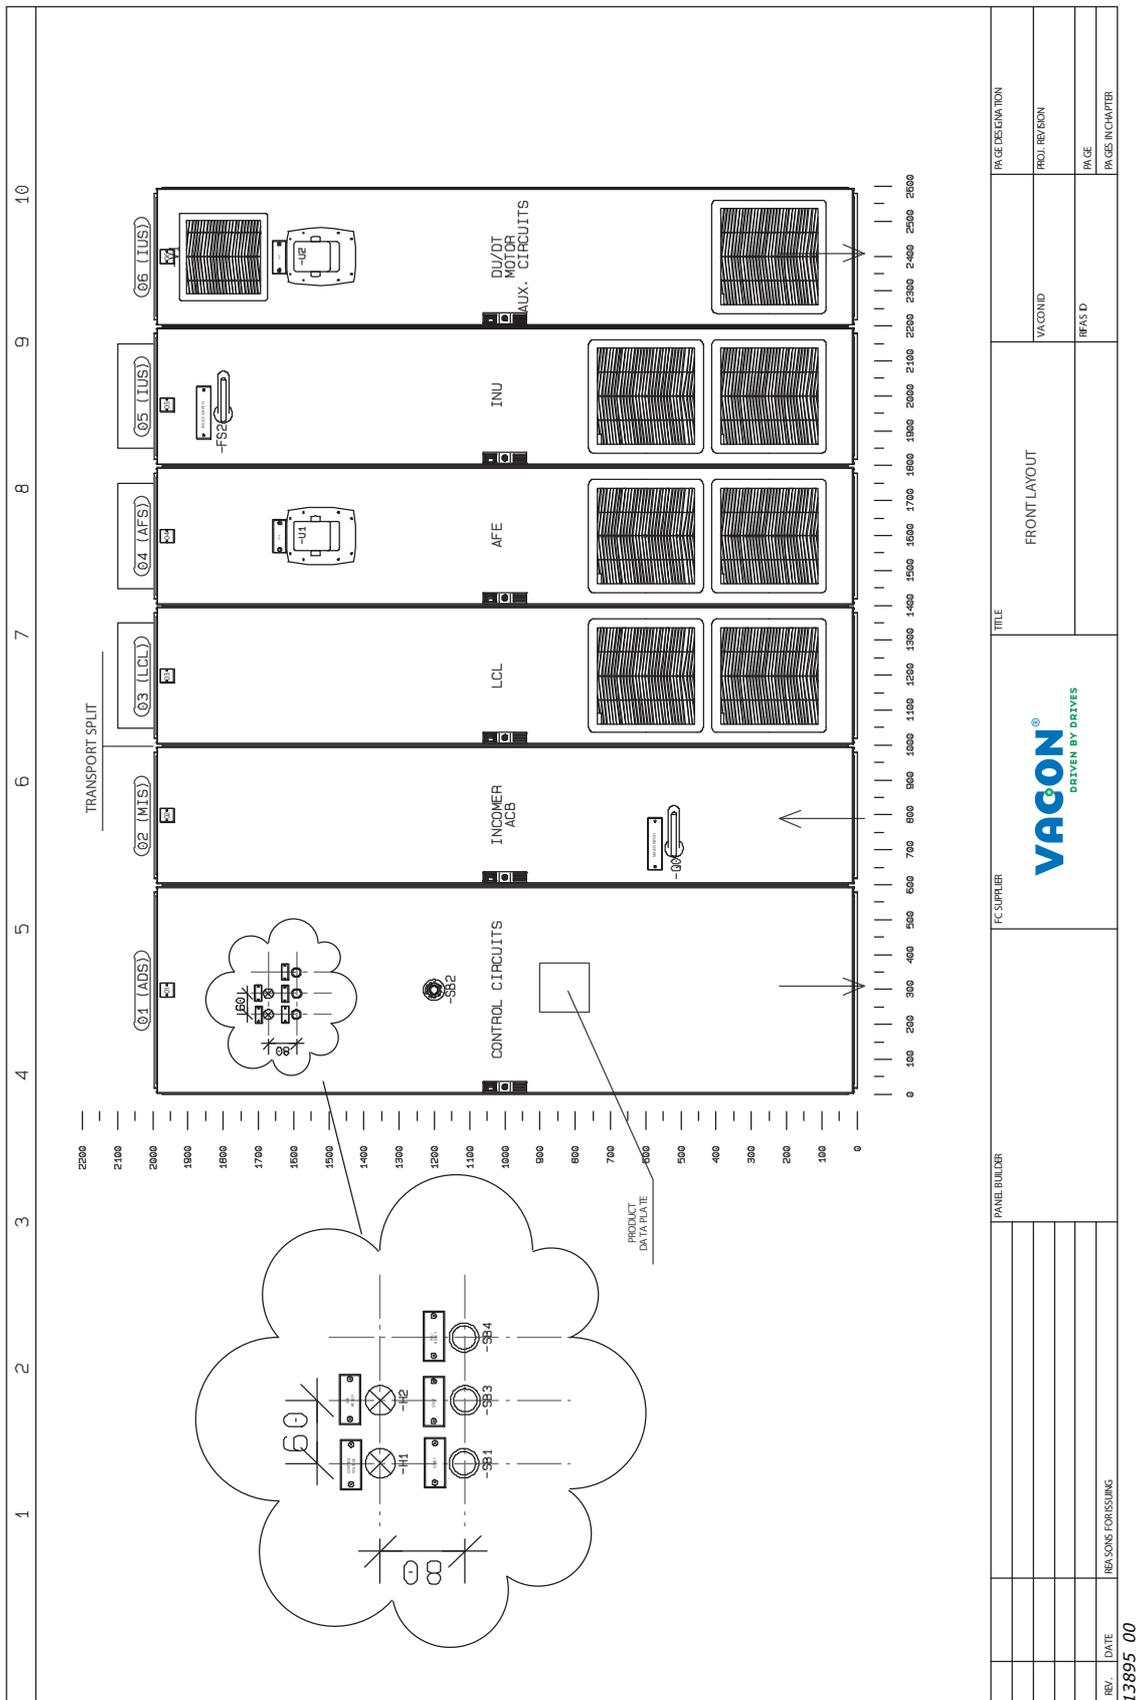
Exemple : plan d'installation de l'appareillage de commutation
